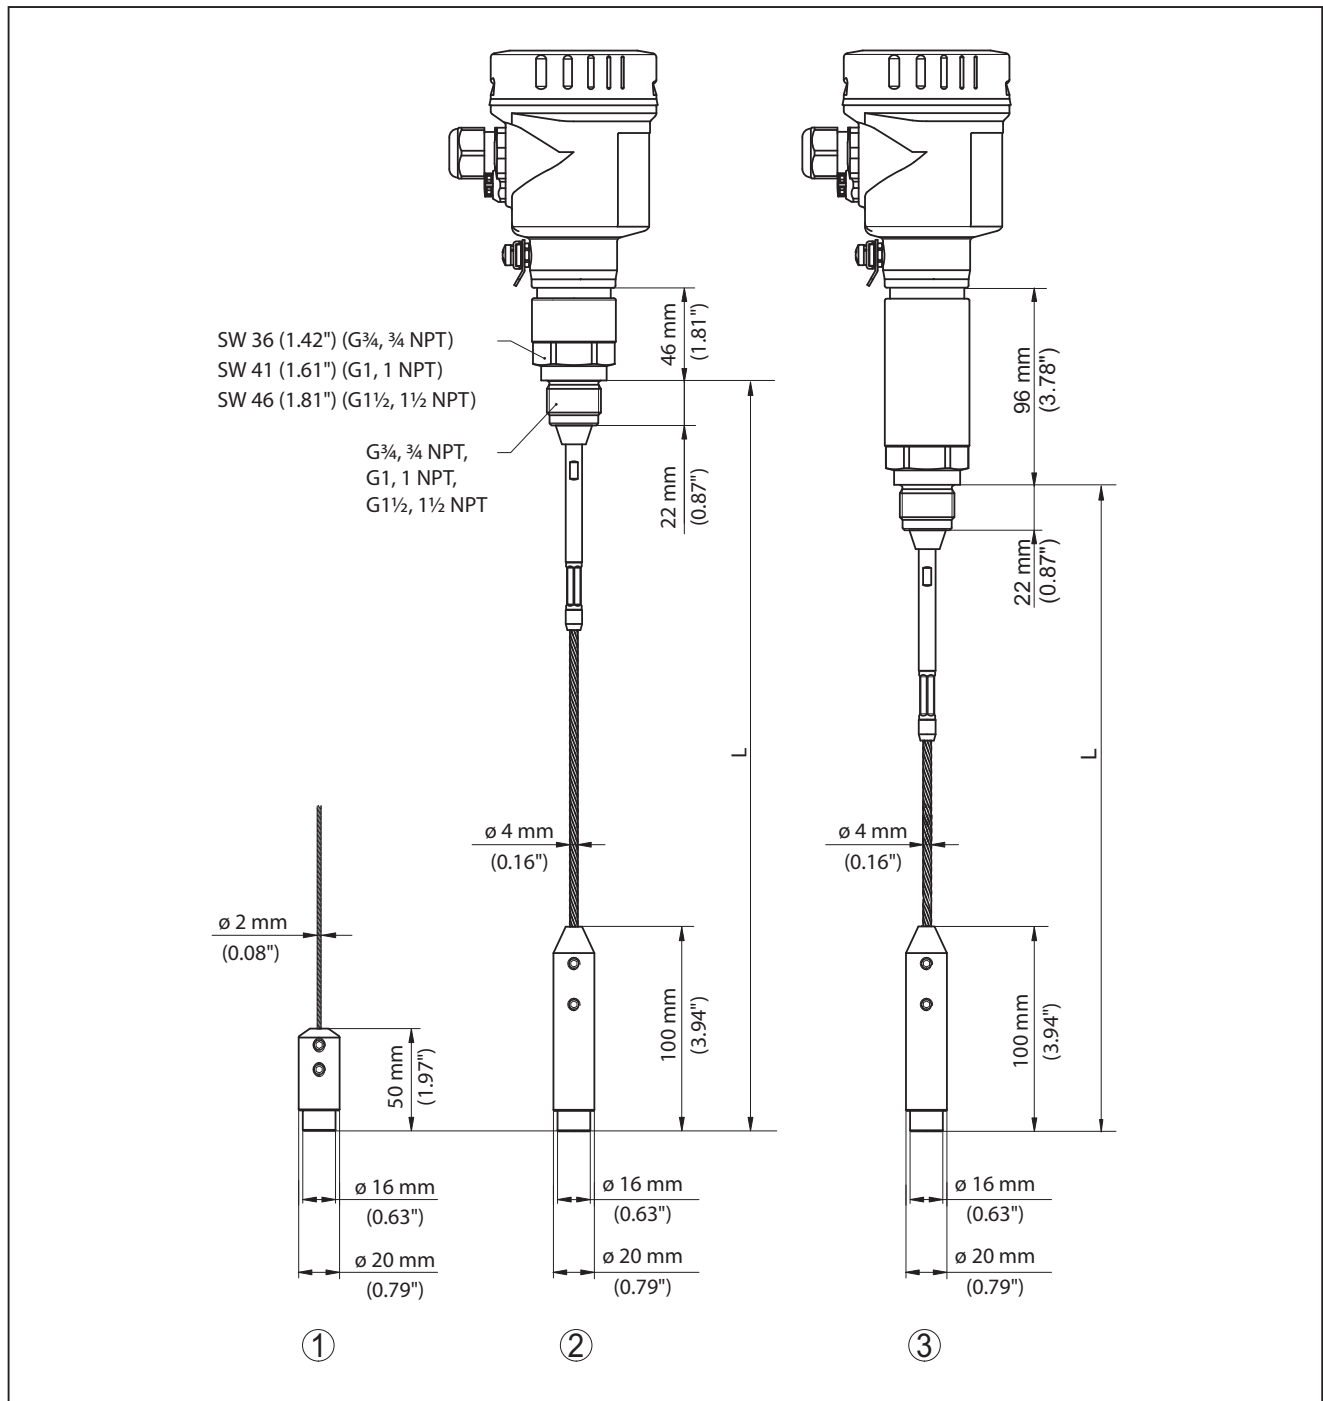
BMD 1L, Gewindeausführung mit Straffgewicht (alle Straffgewichte mit Gewinde M8 für Ringschraube)
